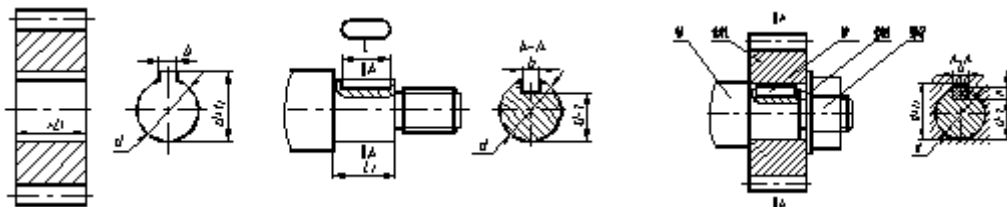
齿轮和轴上键槽的画法及尺寸注法
